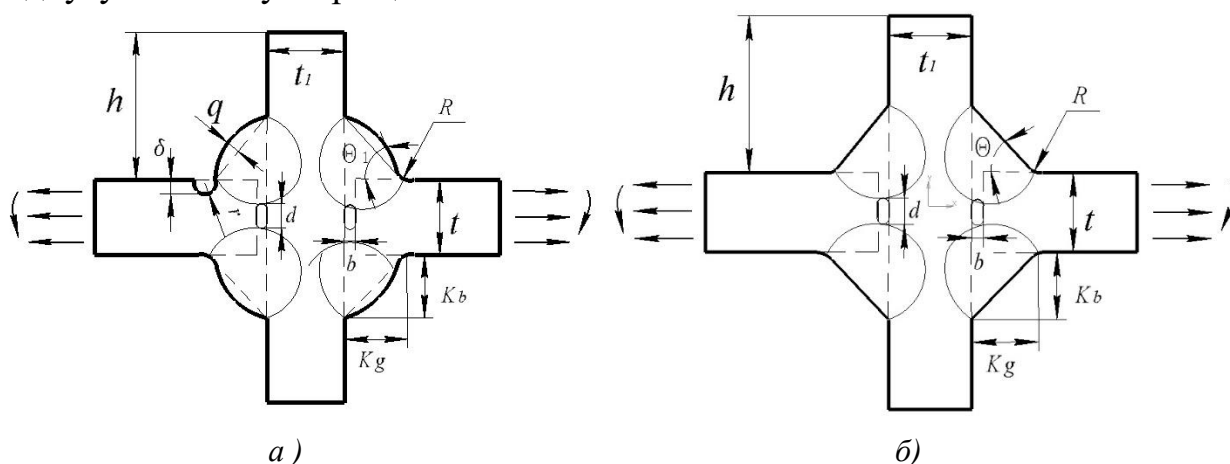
Параметрическая модель крестового сварного соединения при нагружении по разрезному элементу растягивающей и изгибающей нагрузкой: а) - с усилением шва, б) – без усиления шва
